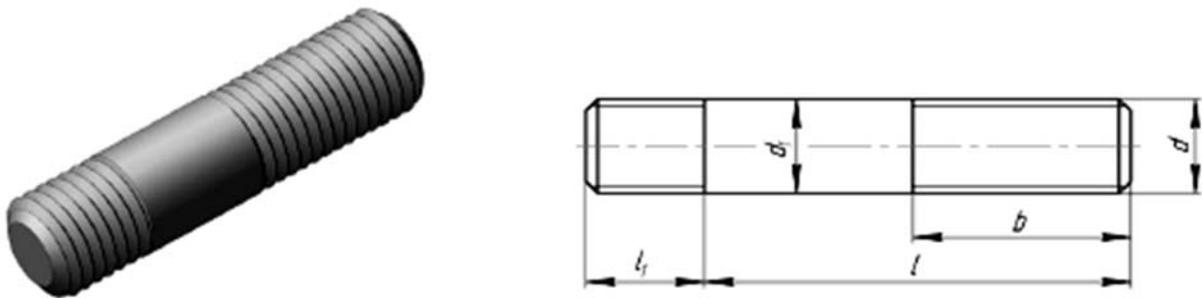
Шпилька общего назначения исполнения 1
